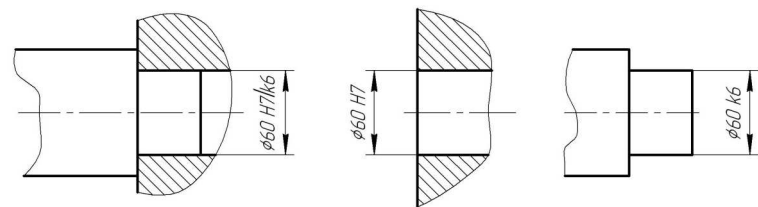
б. Спряження вала з отвором, допуск отвору та допуск вала.
